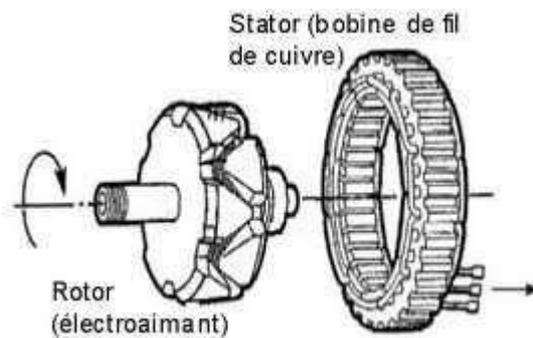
Stator et rotor d'une machine synchrone [20]
